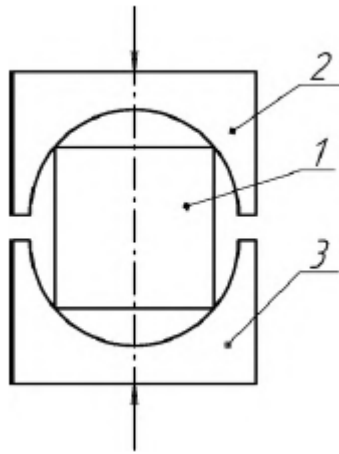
Переформування заготовок осаджуванням на ребро 1 - заготовка; 2 - пуансон; 3 – матриця
